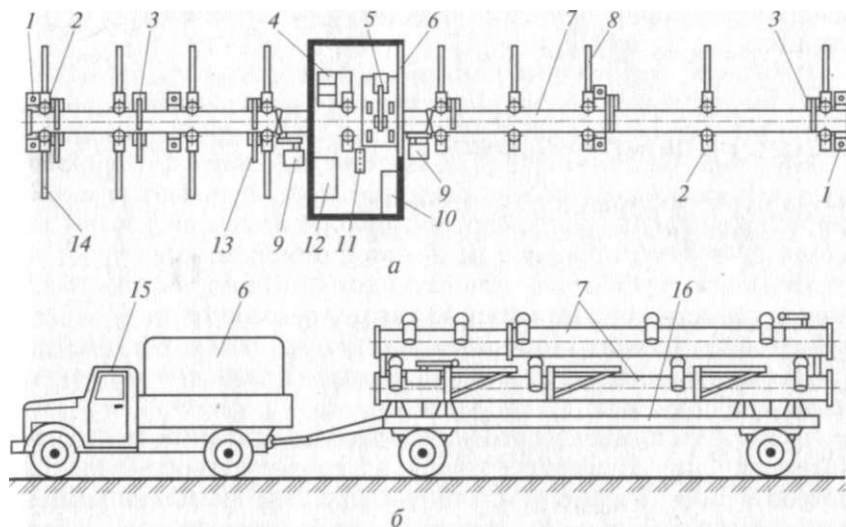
Схема передвижной установки для сборки и сварки секций трубопроводов с $\text{Ц} = 80 \dots 600$ мм в рабочем (а) и транспортном (б) положениях:
